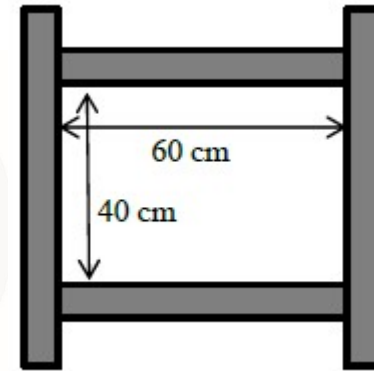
Dimensions de la plaque d'essai
